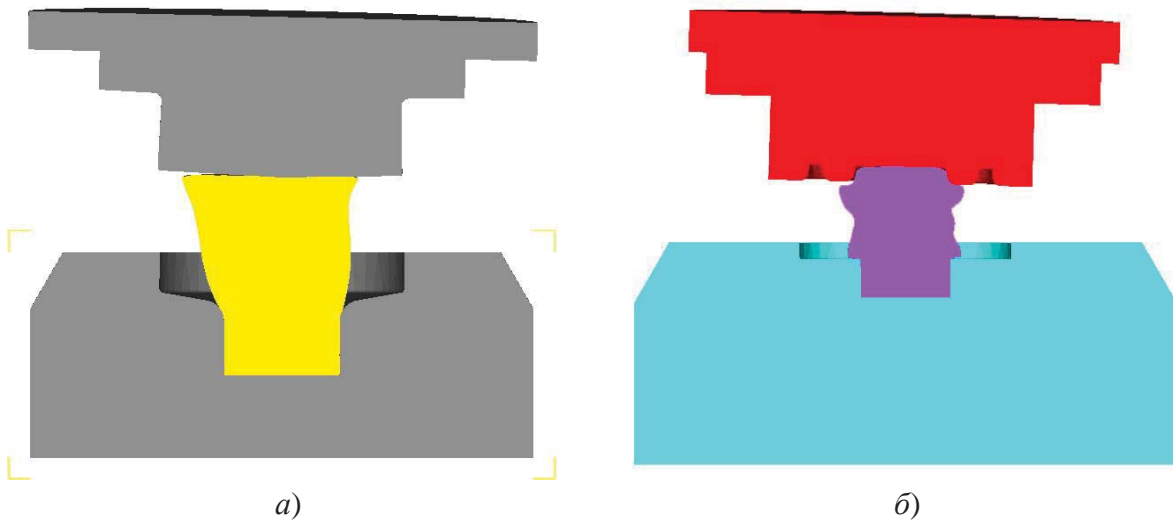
Дефекты, возникающие при сферодвижной штамповке заготовок:
